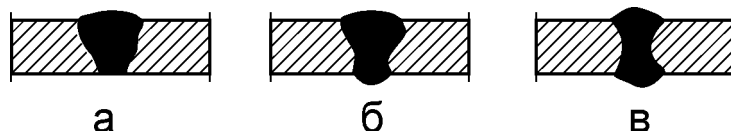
Типы сварных швов: а -стыковой односторонний; б – стыковой с подваркой; в – стыковой двухсторонний
